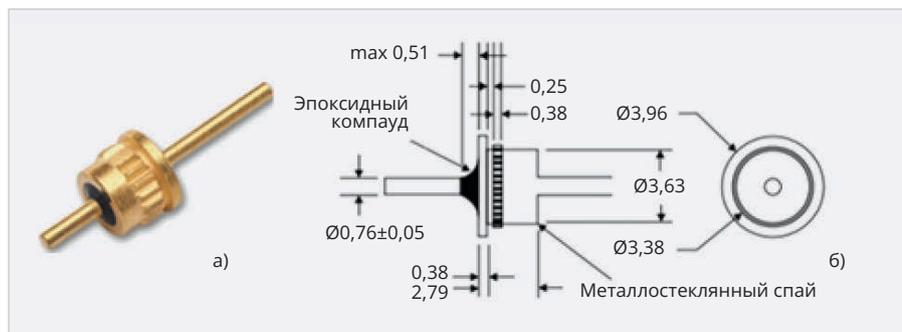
Фильтр для прессовой посадки в корпус изделия. Внешний вид (а), конструкция (б)
